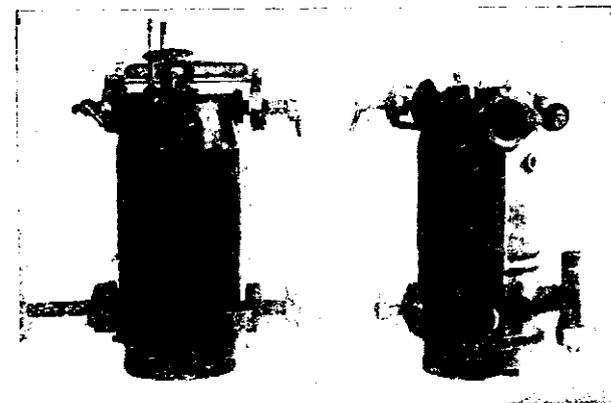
Цилиндры мотора М-17, подготовленные для испытания рубашек.
